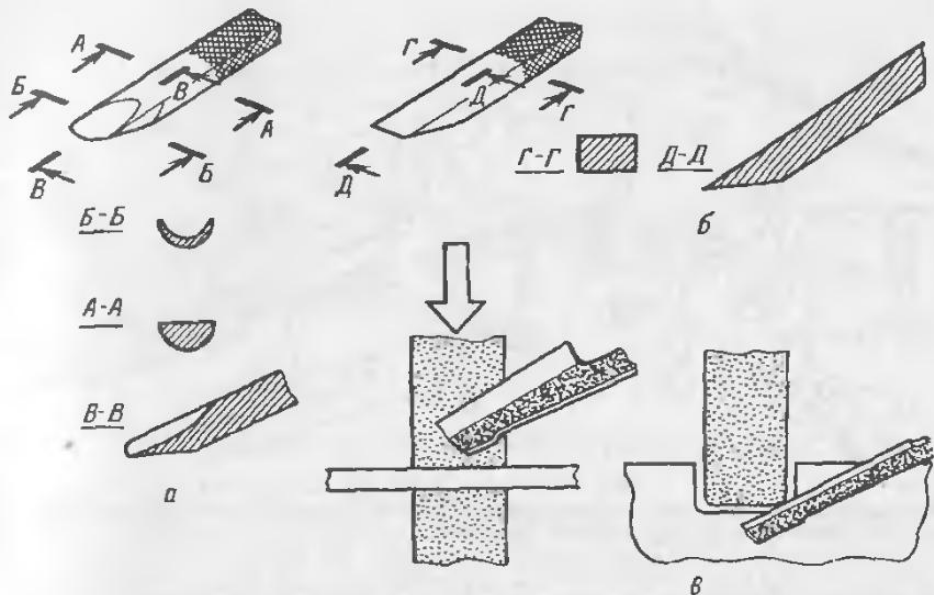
Изготовление и заточка инструмента: а - полукруглых стамесок; б - плоских стамесок; в - бритвенная заточка лезвия ножа
